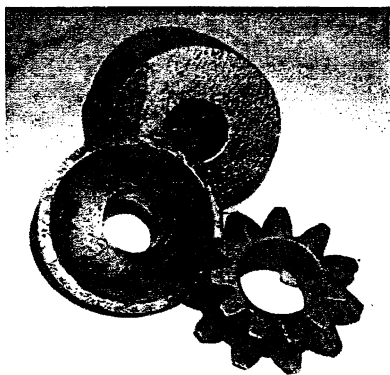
Литая заготовка, поковка и готовая шестерня дифференциала МАЗ-5336 из чугуна (дет. 5336-2403056)
